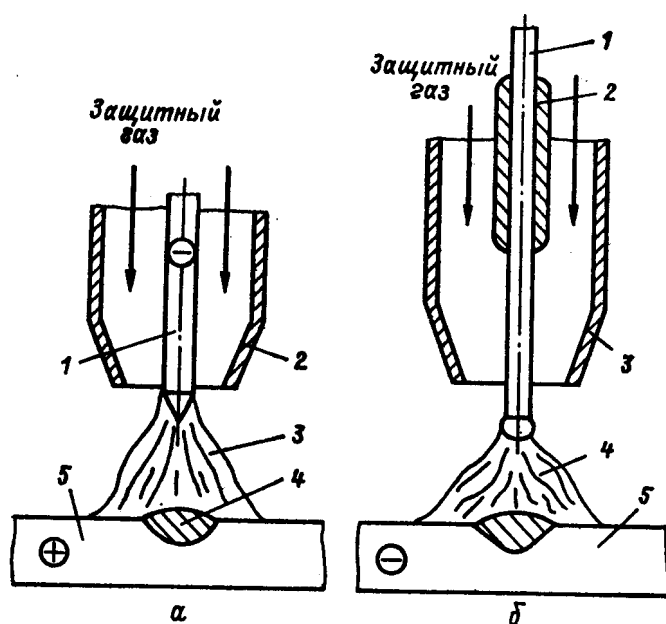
Схема процесса сварки в среде защитных газов:
